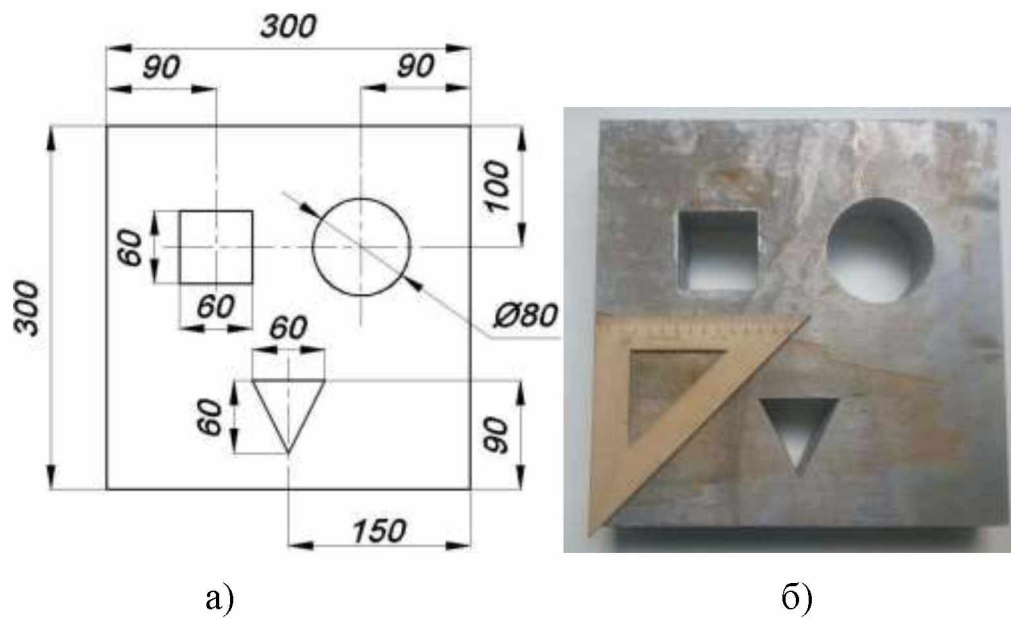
Деталь для визначення точності: а) креслення б) вирізаний зразок з алюмінію
